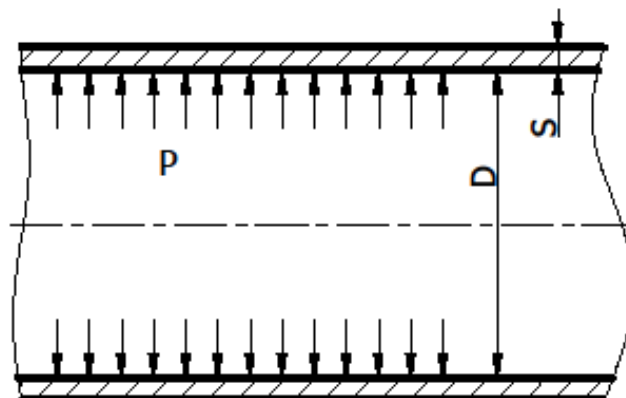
Розрахункова схема циліндричної обичайки
